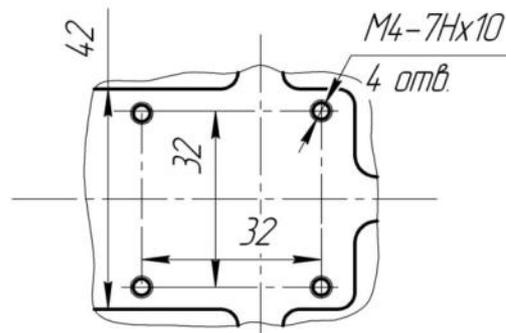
Присоединительные размеры под установку датчика вибрации
